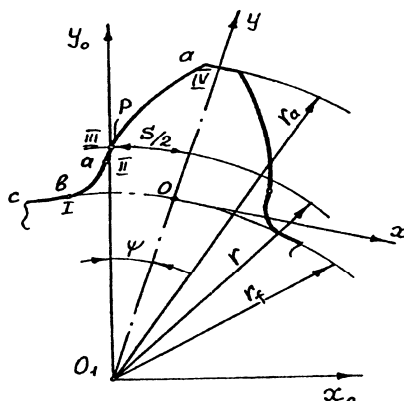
Расчетная схема для расчета эвольвентного профиля детали
